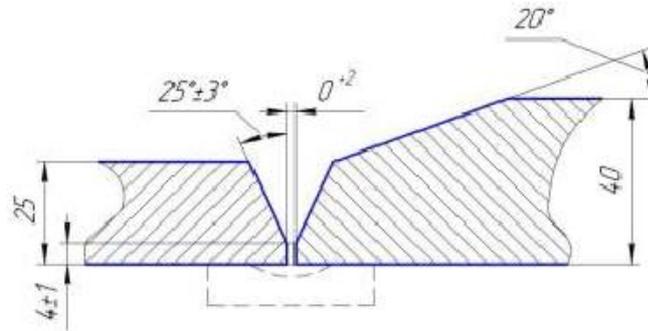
Конструктивные элементы подготовленных кромок сварного соединения
